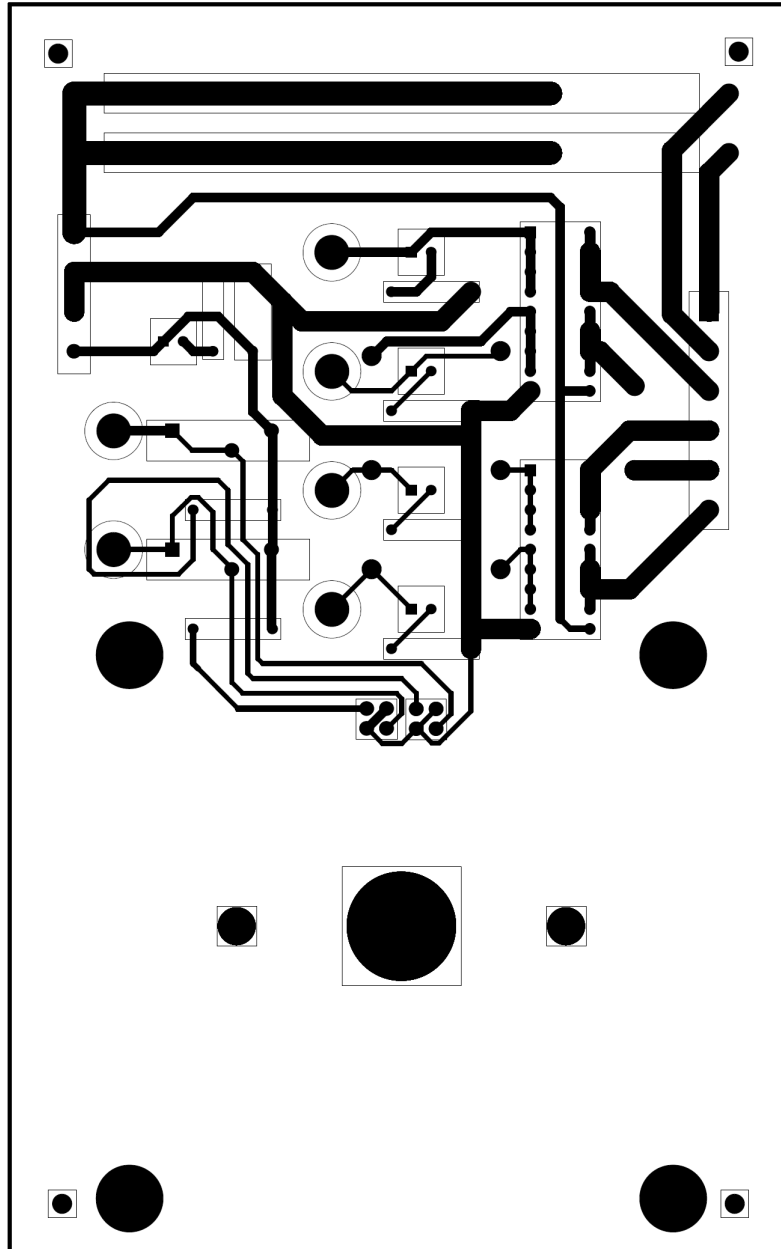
Capa inferior (BOT) de la PCB de la interfície per al motor unipolar
